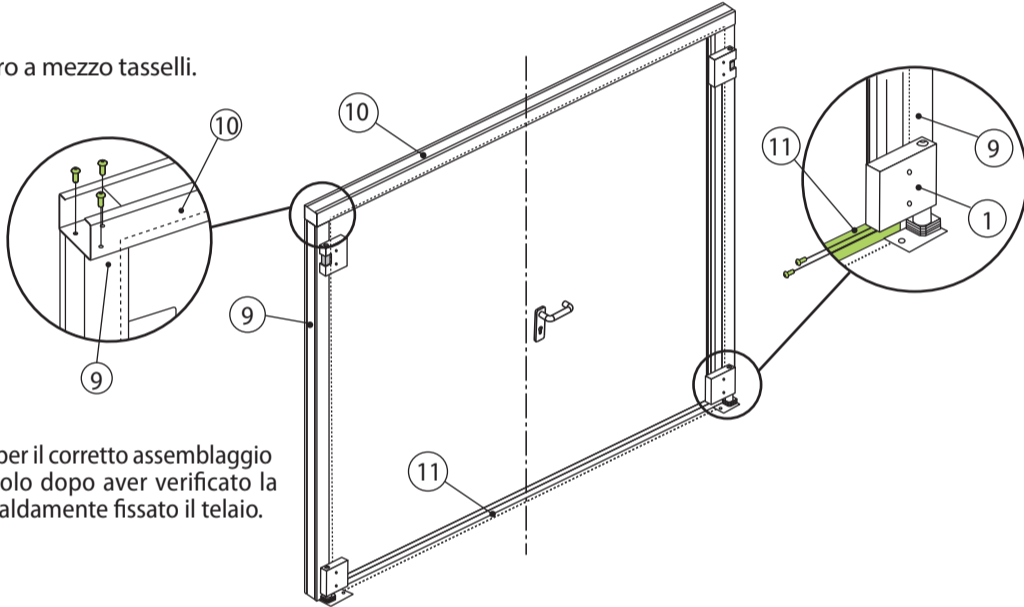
ASSEMBLAGGIO TELAIO - ANTA
